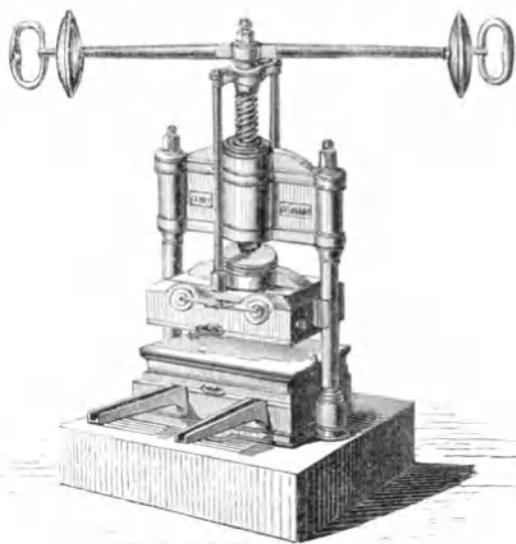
Vergoldepresse aus der Maschinenfabrik der Gebrüder Heim in Offenbach.
